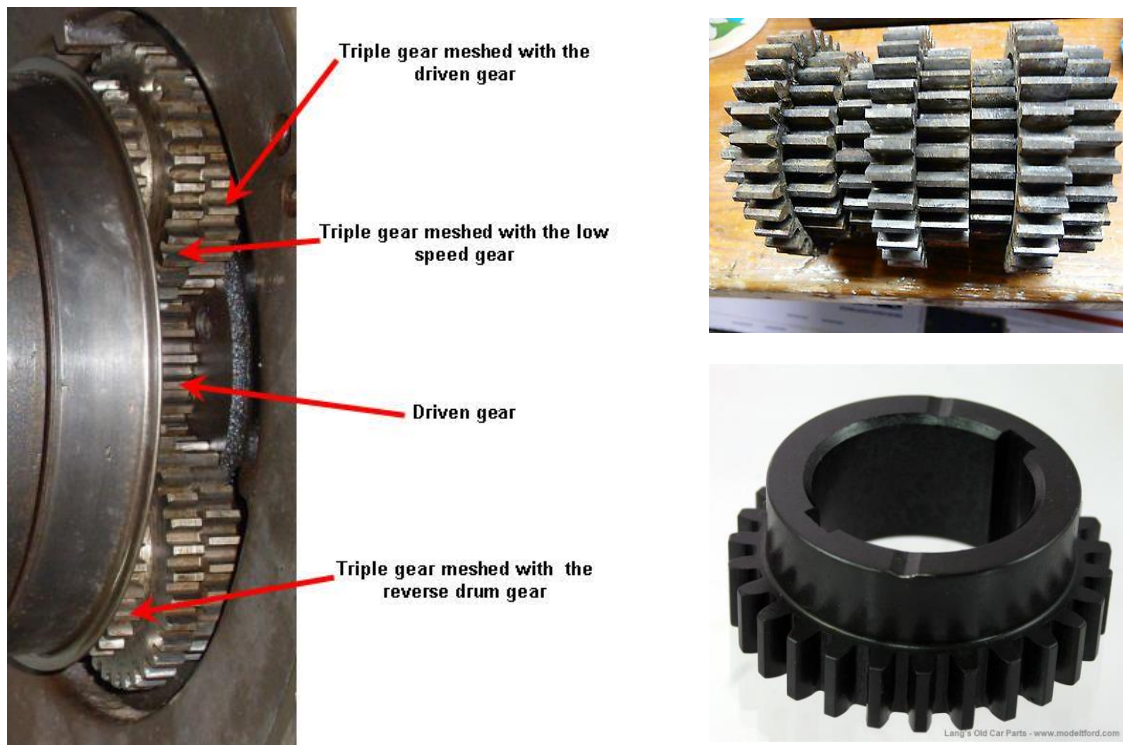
Engranaje conducido y triples engranajes: instalados (izquierda) [6] y pieza individual (derecha) [69,70]
